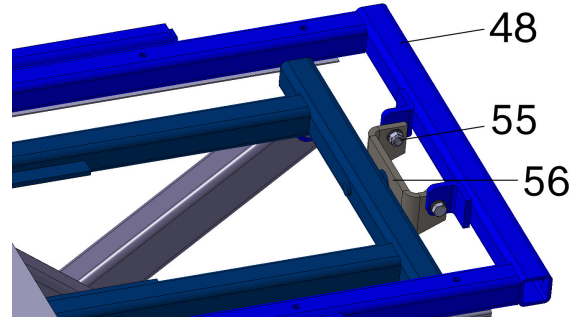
Ножничный подъемный стол без платформ, вид сверху
